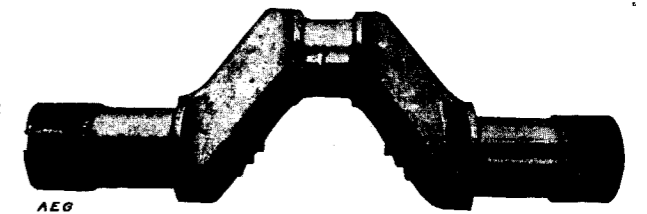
ª—Cigüeñal reforzado con soldadura por arco.
